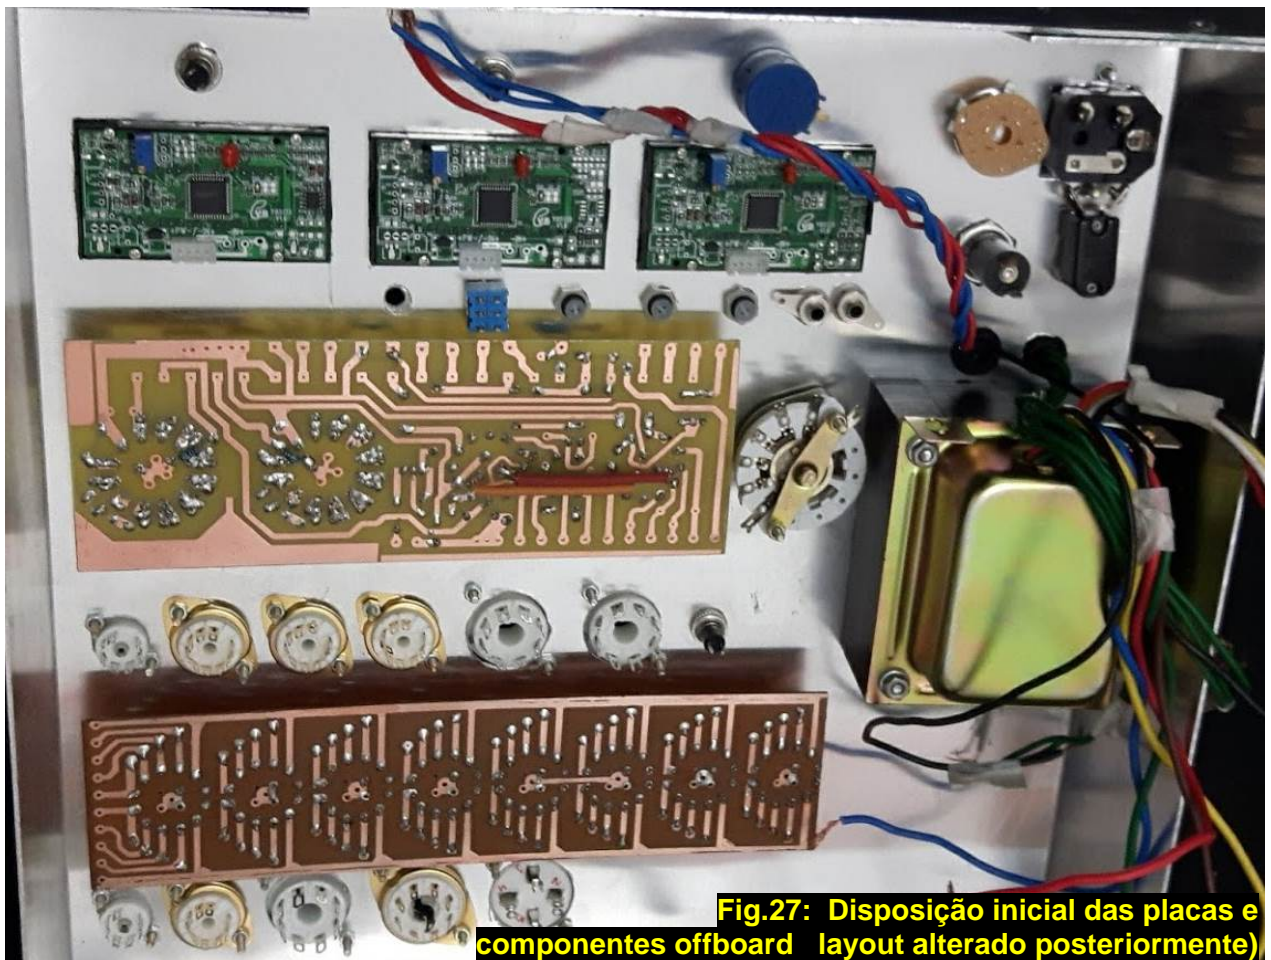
Disposição inicial das placas e componentes offboard layout alterado posteriormente)
